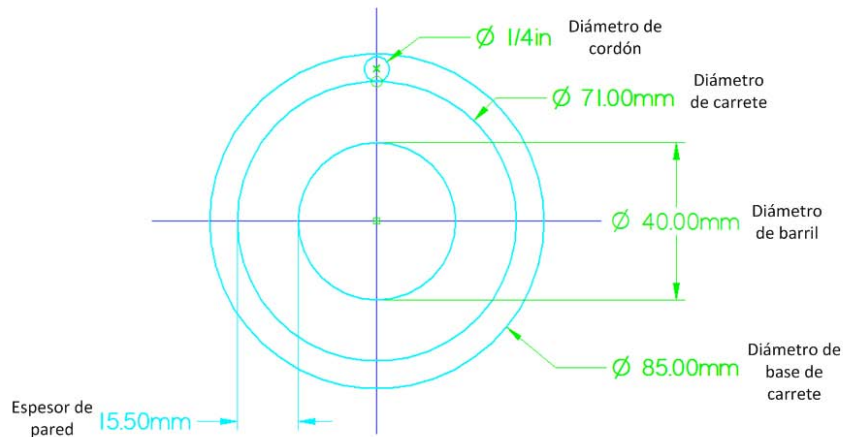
Dimensiones transversales de carrete rebobinador.
